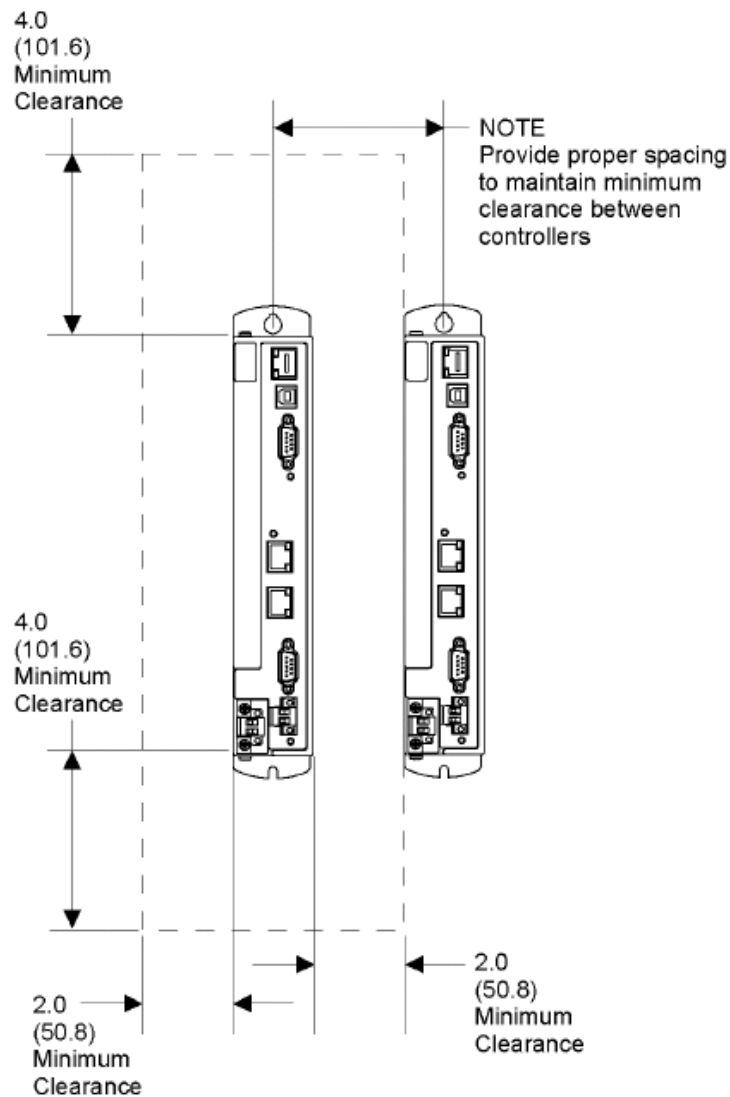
Dimensiones sugeridas para montaje de controlador ACR 9640, pulgadas (mm) [53].
